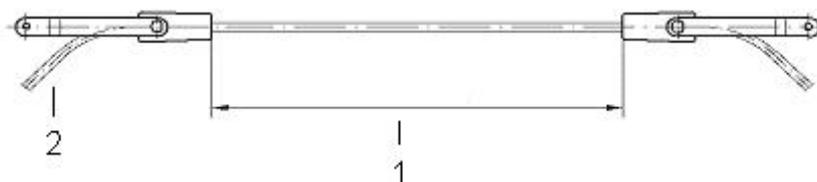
Схема испытания натяжного зажима для проверки разрушающей нагрузки зажима и прочности заделки провода
